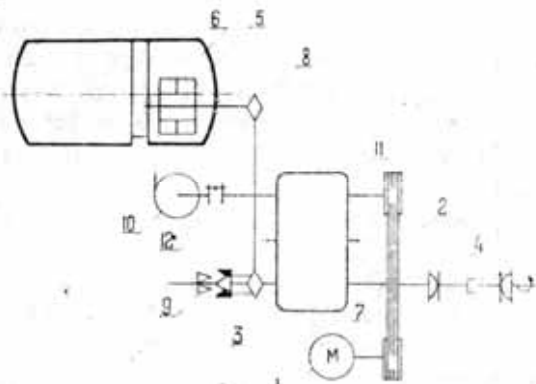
Схема привода рабочих органов агрегата АПЖ-12:
